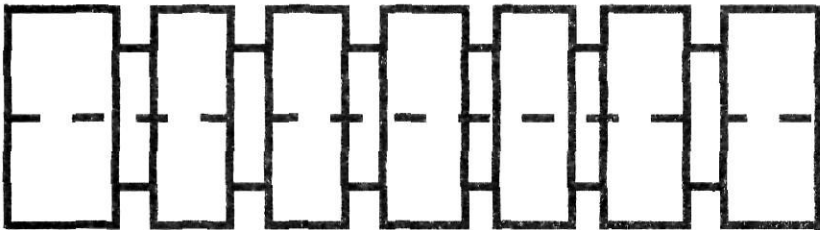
Общий вид заготовки для определения эффективности стружкодробления
